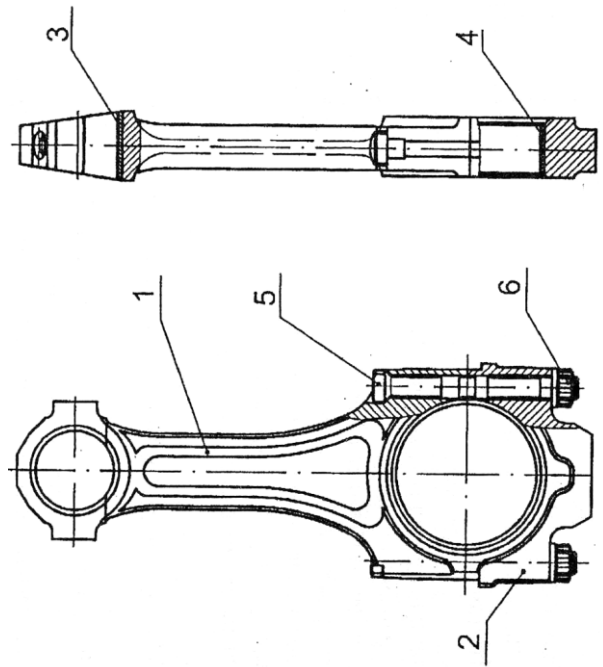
Шатун двигателя КамАЗ-740
